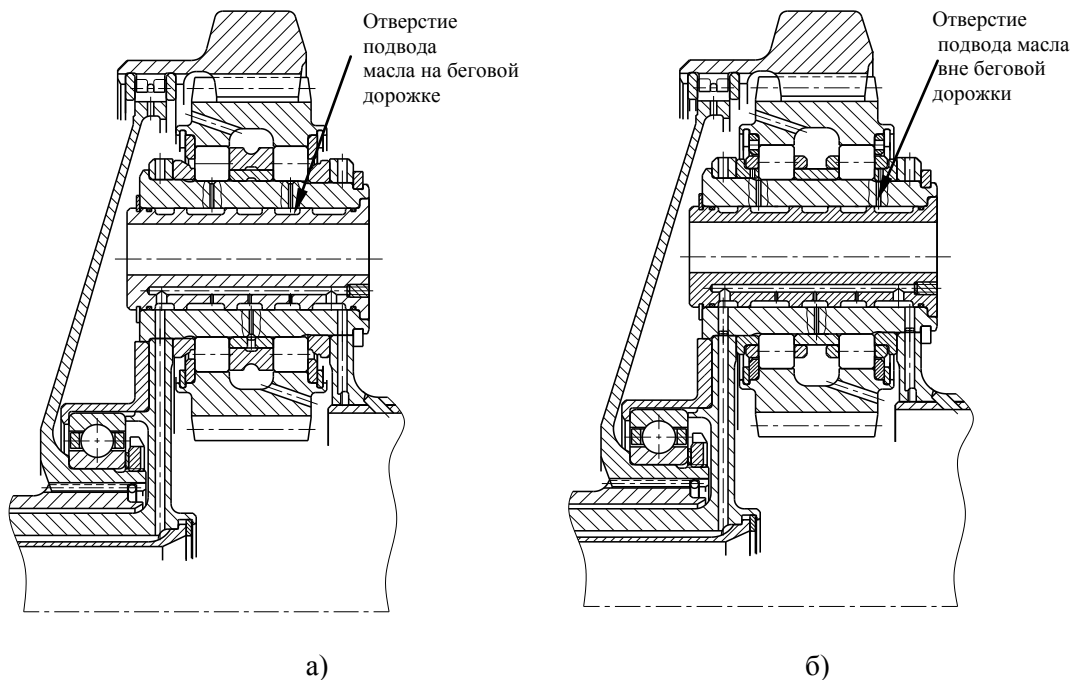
Схема подвода смазки в подшипники главного редуктора двигателя ТВЗ-117ВМА-СБМ1: а) исходная конструкция; б) доработанная конструкция подшипника сателлита
